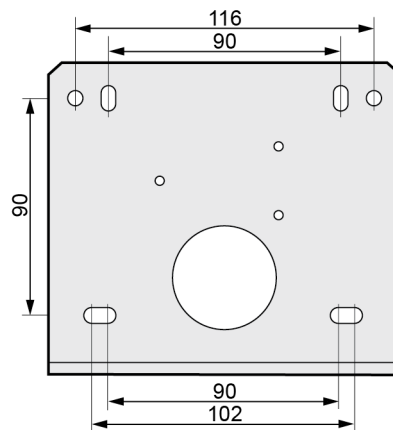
plan de perçage pour fixation murale (vue de la face plaquée au plafond).
